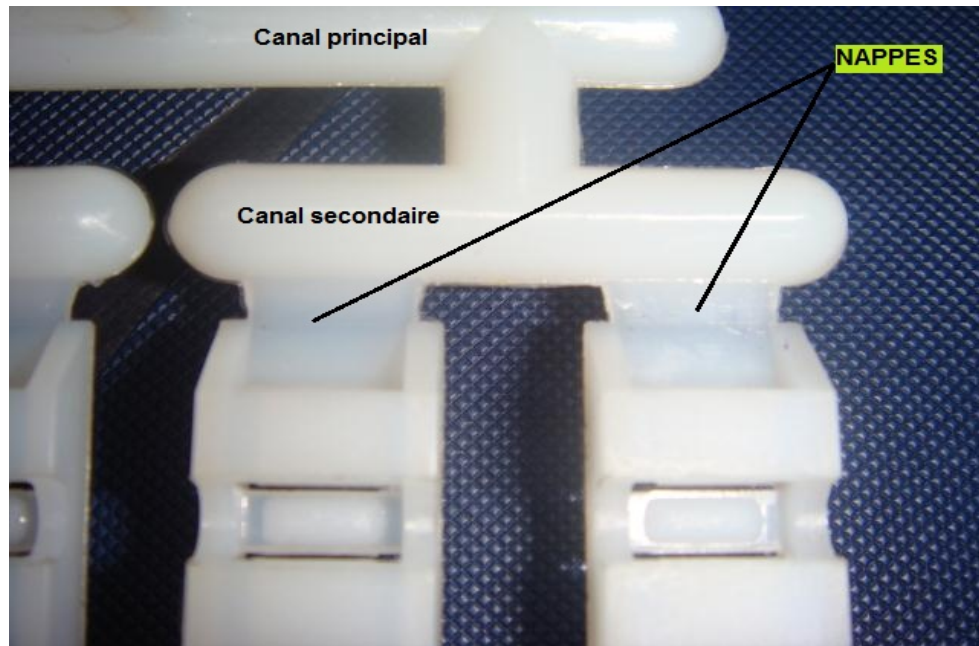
Gros plan sur les nappes et les canaux d'alimentation
